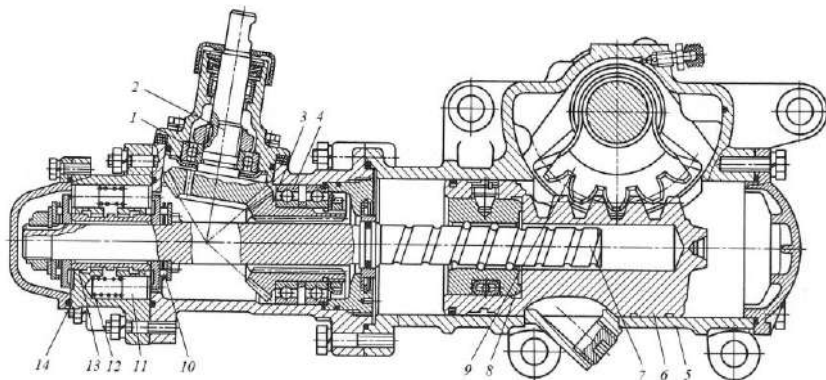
Рульовий механізм з шестеренним редуктором та передачею «гвинт – кулькова гайка – рейка – зубчастий сектор»:
